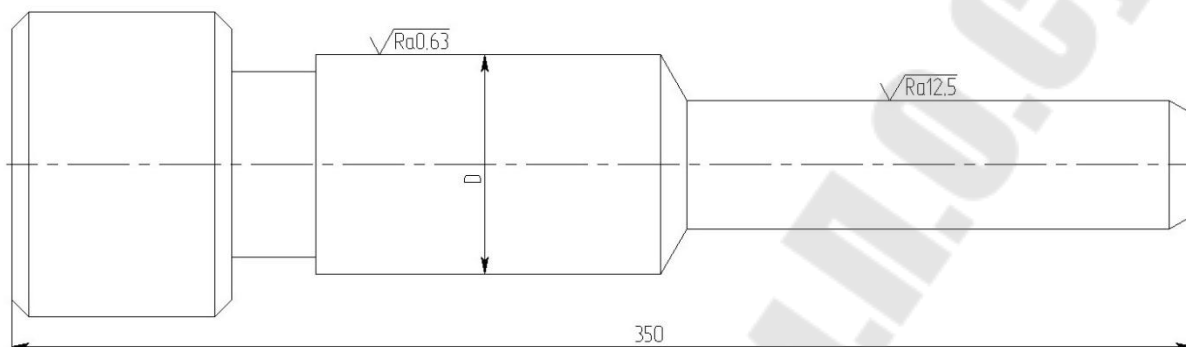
Вал ступенчатый (материал – группа стали М1 или М2; заготовка – штамповка на ГКМ)
